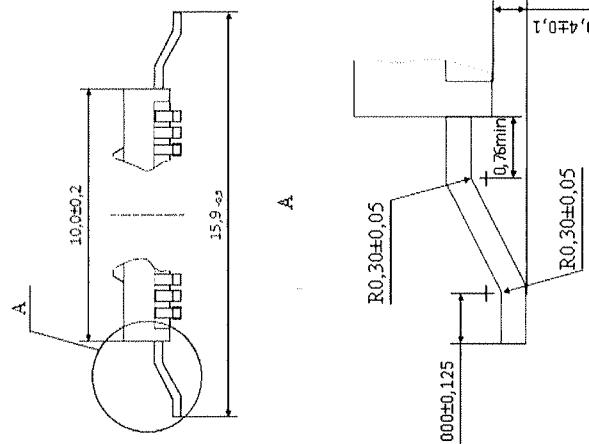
Рекомендуемый вид формовки и обрезки выводов микросхемы 5529TP024
